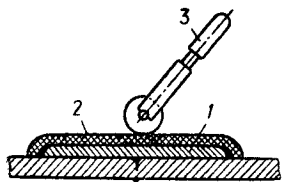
Замазування тріщини в корпусній деталі епоксидною композицією:
